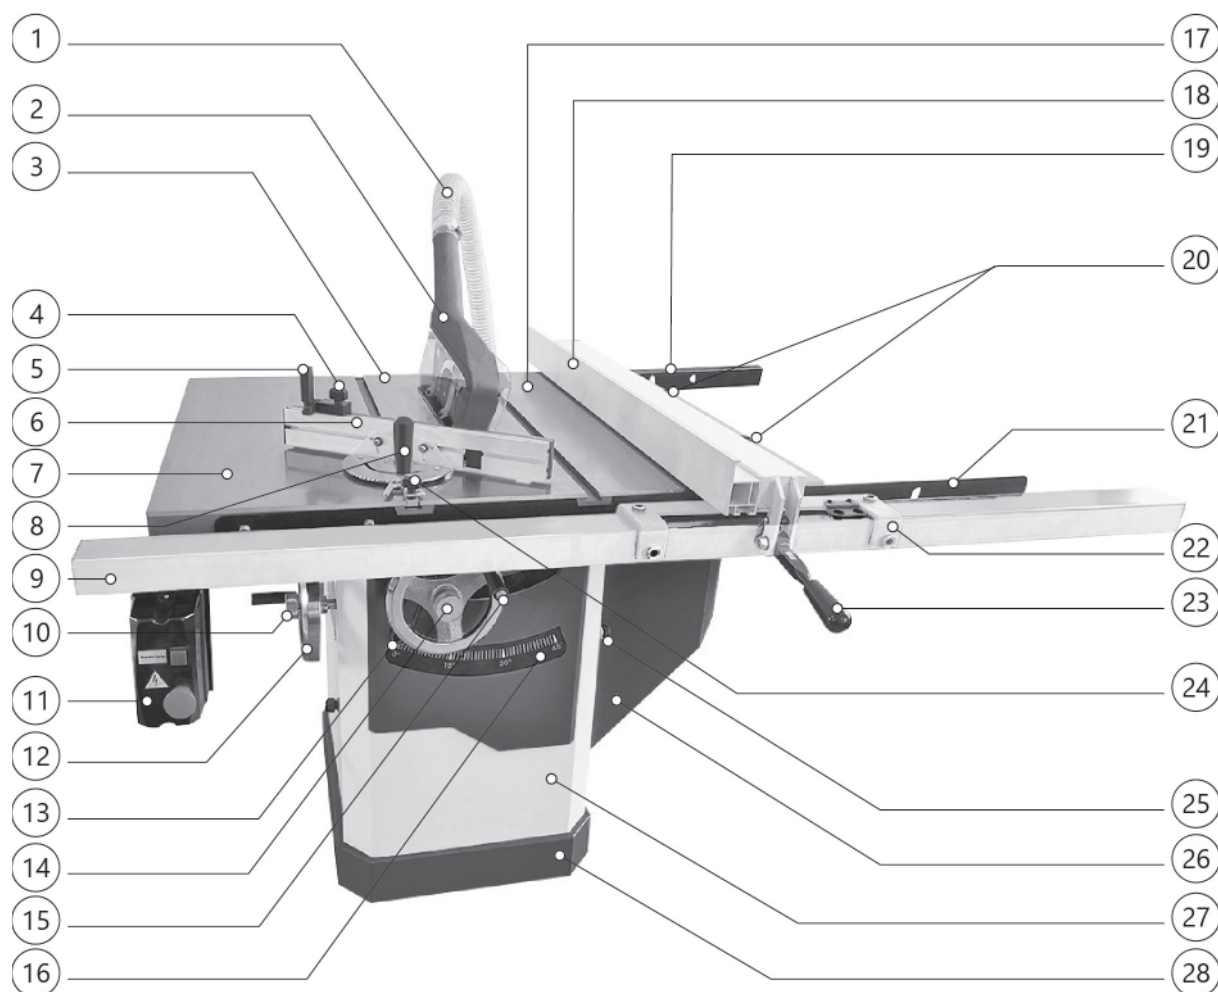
Основные элементы станка BELMASH LTS-250P/400.
